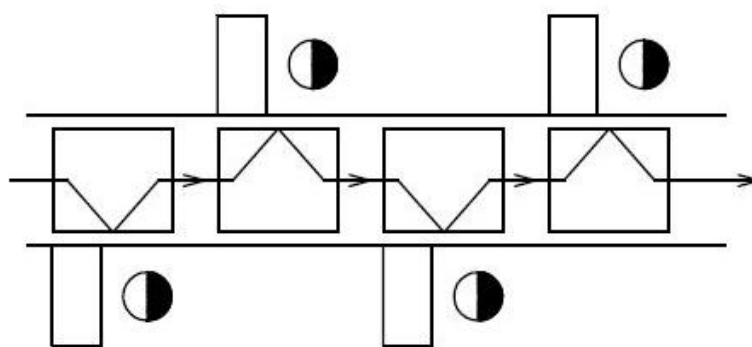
Oboustranná jednosměrná montážní linka [2].
